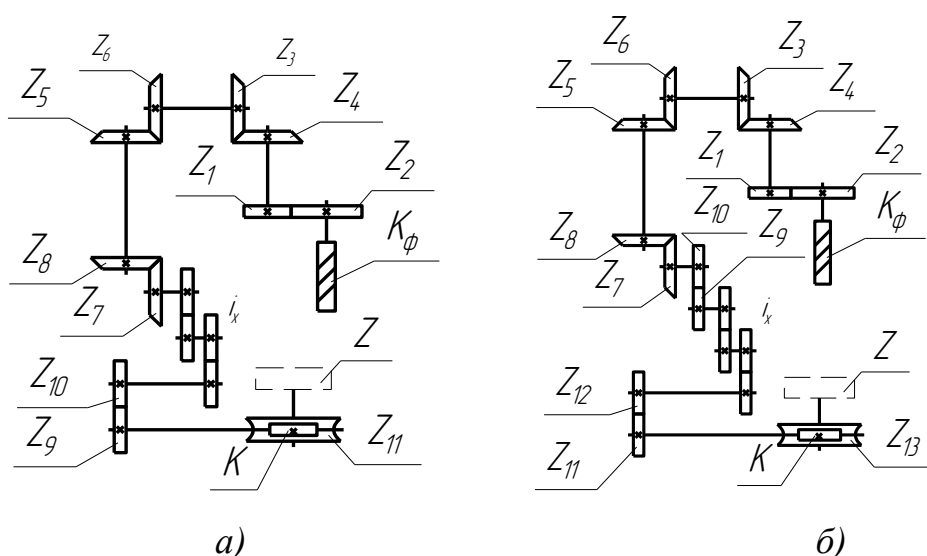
Кінематичні ланцюги обкатки (ділення) зубофрезерного верстата
